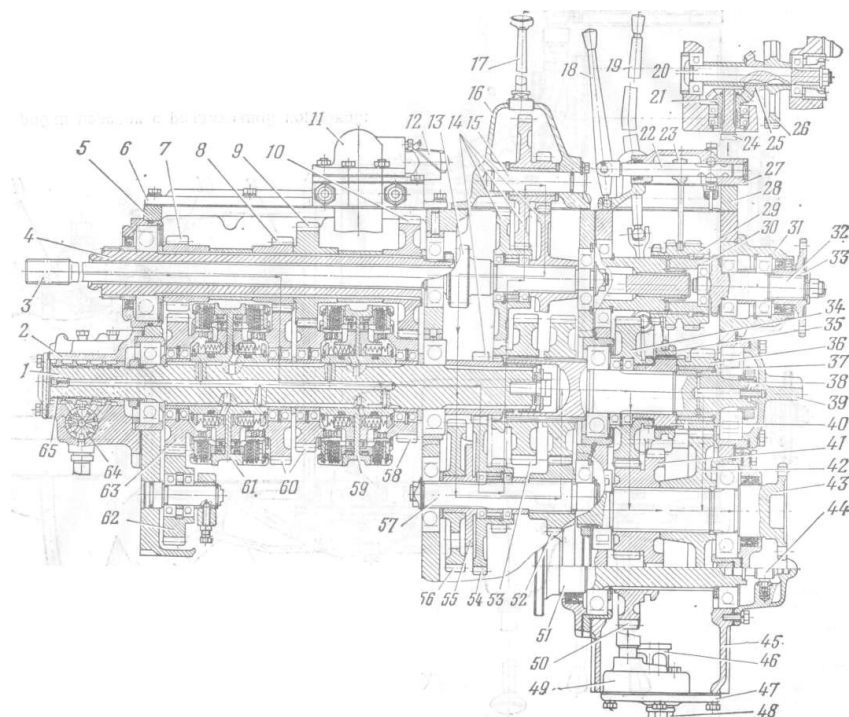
Коробка передач з роздавальною коробкою в зборі: 1 - вторинний вал; 2 - розподільник; 3 - проміжний вал; 4 - первинний вал; 5 - корпус коробки передач; 6 - кришка; 7 - ведуча шестерня задньої передачі; 8 - провідна шестерня першої передачі; 9 - провідна шестерня другої передачі; 10 - провідна шестерня
